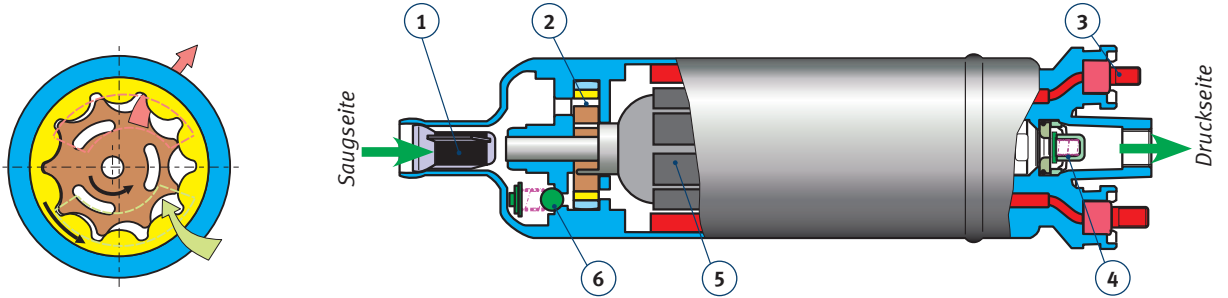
Pumpenprinzip und Schnitt (schematisch) durch eine Zahnringpumpe
